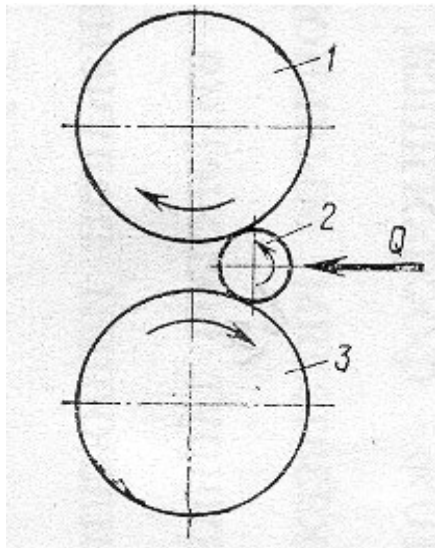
Схема поперечної прокатки: 1 – верхній валок; 2 – прокатний виріб; 3 – нижній валок
